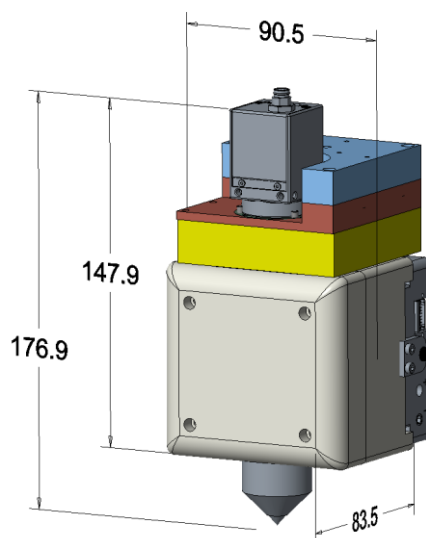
Dimensions físiques (en mm) del sensor complet.
